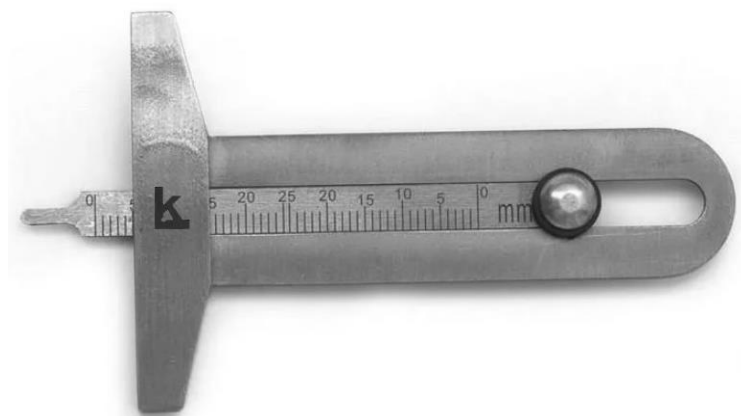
Общий вид штангенглубиномеров модели ИВП
